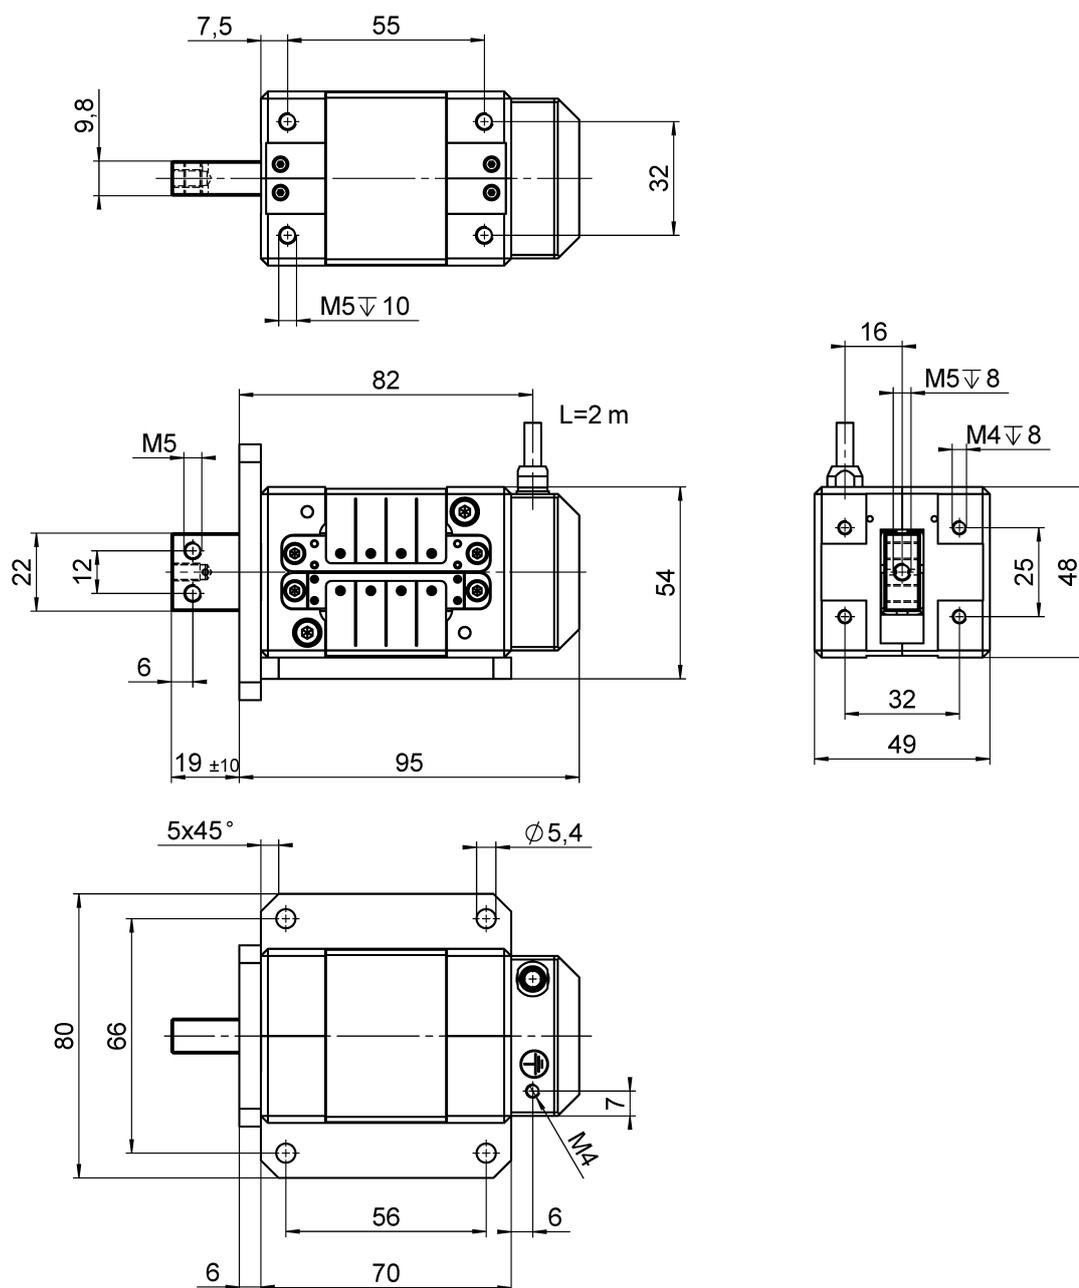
Abmessungen N-216 (alle Modelle), Läufer in Mittelstellung. Ansicht teilweise mit Montageflansch.
